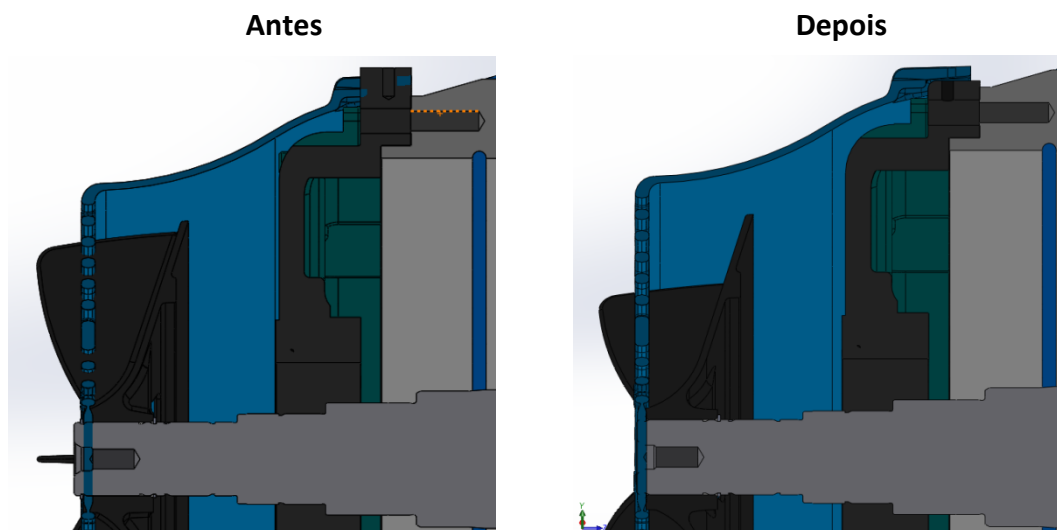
Antes e depois da Tampa Traseira ser maquinada
